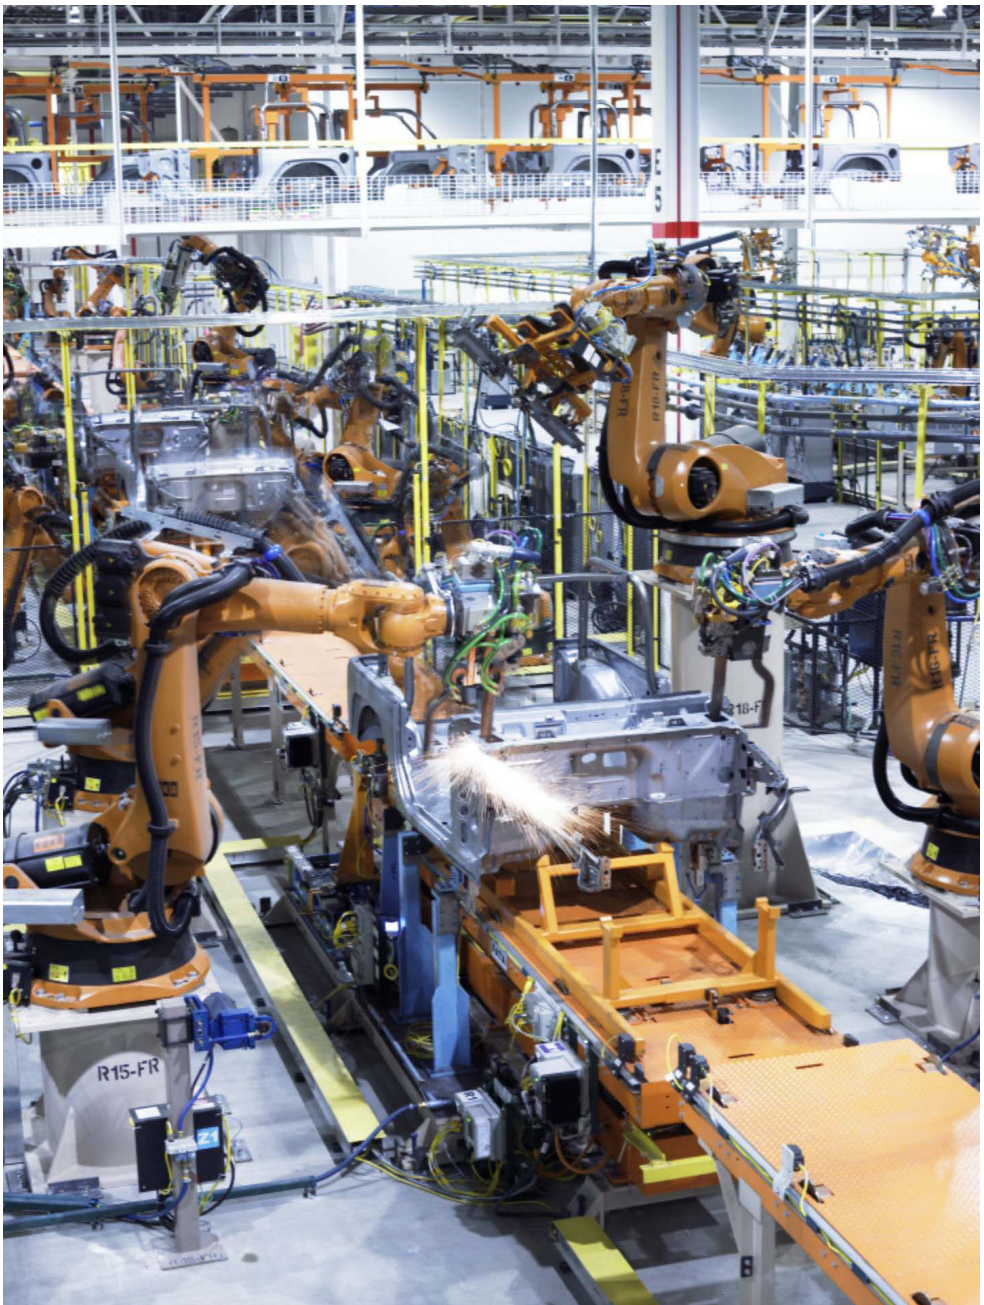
Typischer vollautomatisierter Aufbau für den industriellen Einsatz des Punktschweißens im Automobilbau. An den beiden Roboterarmen im Vordergrund sind die Schweißzangen deutlich zu erkennen. Bei der vom linken Roboterarm ausgeführten Schweißung kommt es im Moment der Aufnahme zur Spritzerbildung. (Mit freundlicher Genehmigung der KUKA Systems GmbH.)
